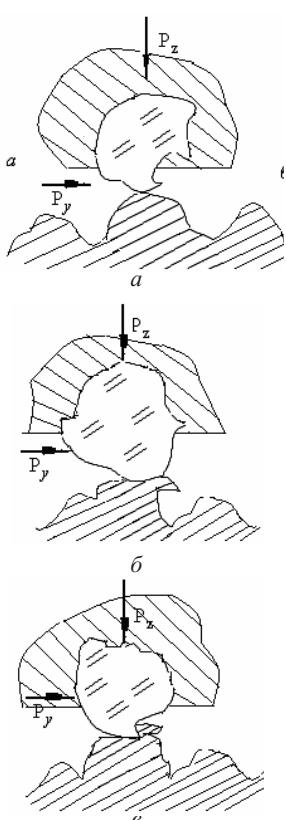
Вид контакта единичного алмазного зерна с выступами шероховатости: а – трение; б – пластическое оттеснение; в – резание
